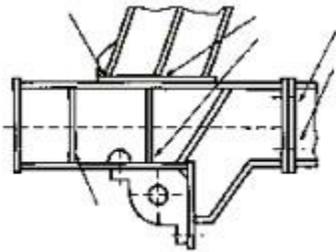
Узел крепления опоры к ходовой тележке козлового крана КДКК-10
